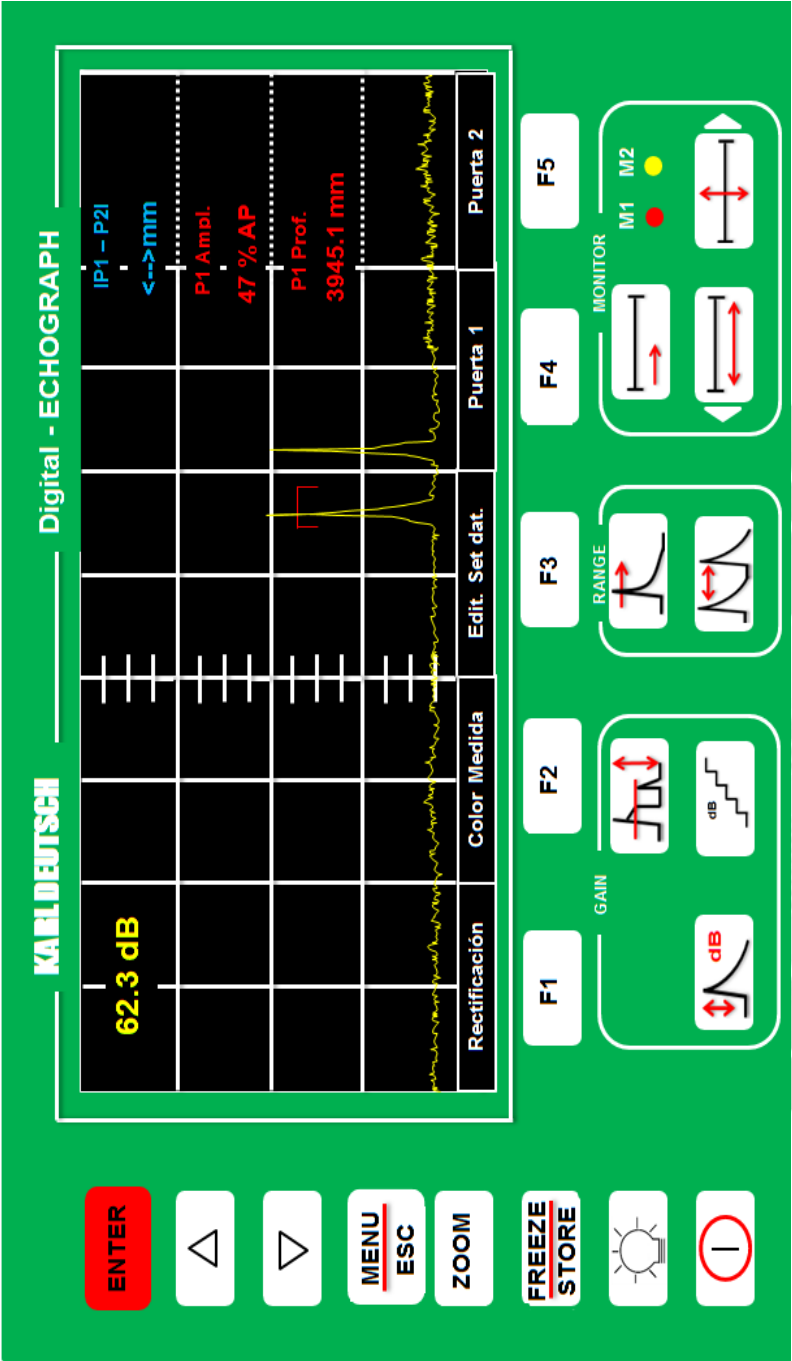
Pantalla de Inspección 1 Fuente SPCC
